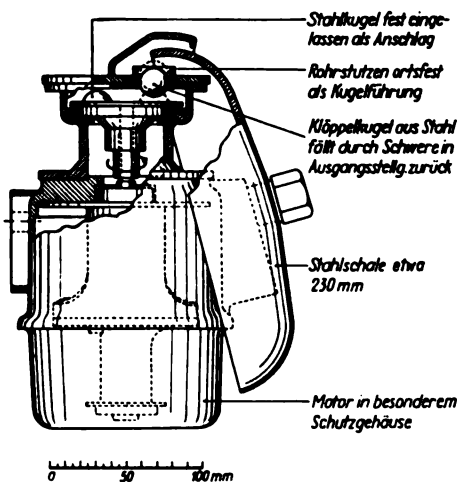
Motor-Kugelwecker von Siemens & Halske.
